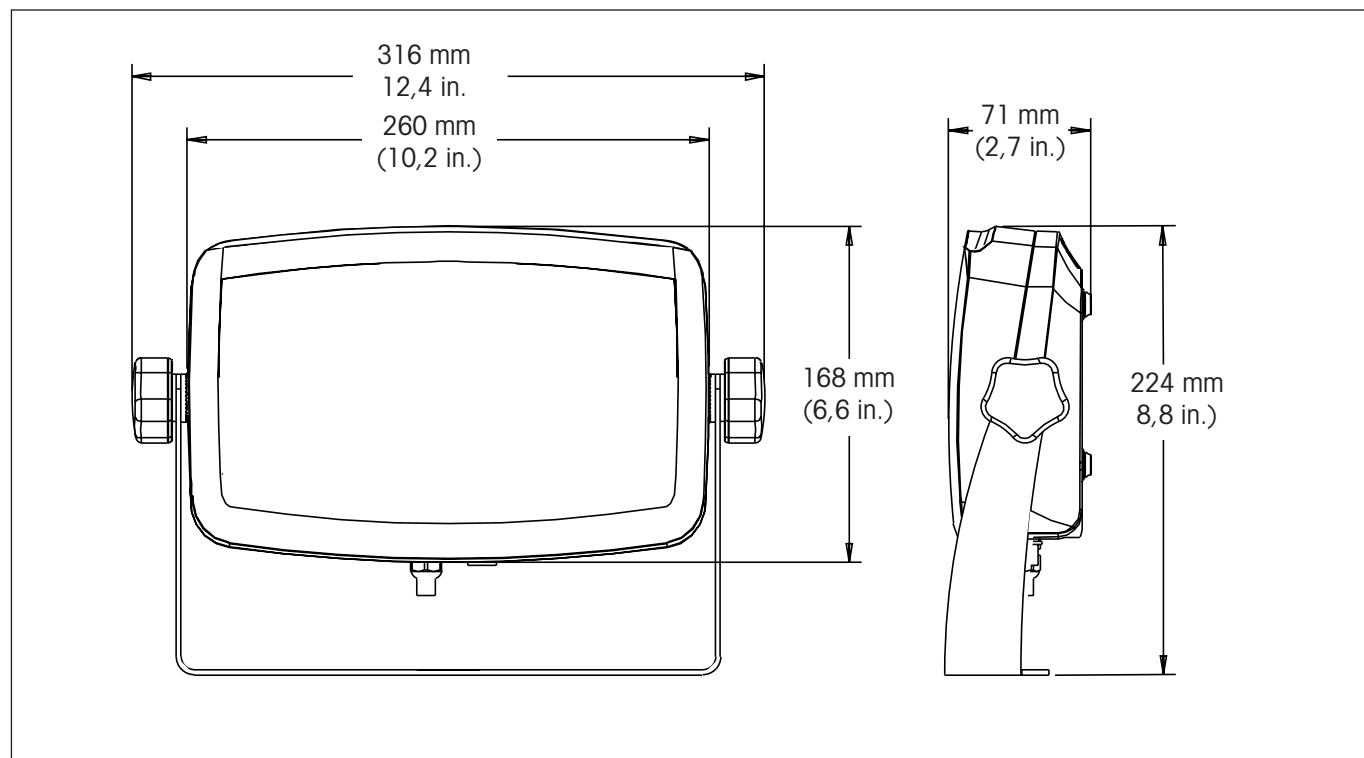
Gesamtabmessungen des T51P-Indikators mit Montagewinkel.
